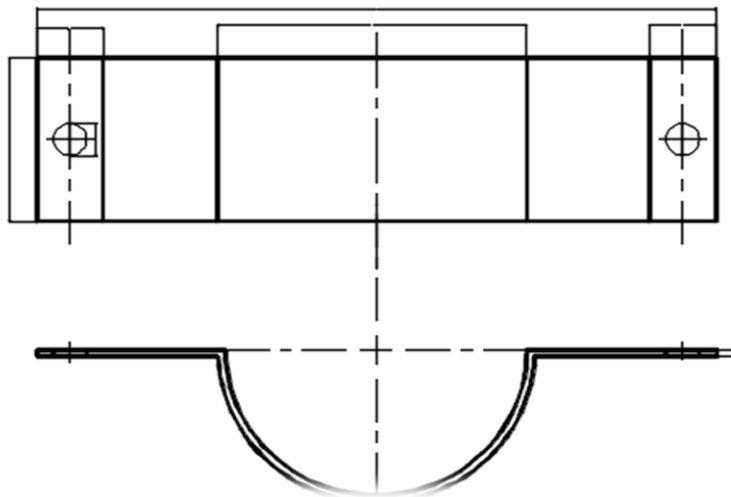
Suporte de fixação e acoplamento do motor (fonte: Autor)
